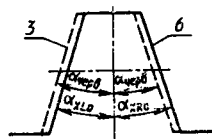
Углы профиля задних поверхностей зубьев червячной фрезы
